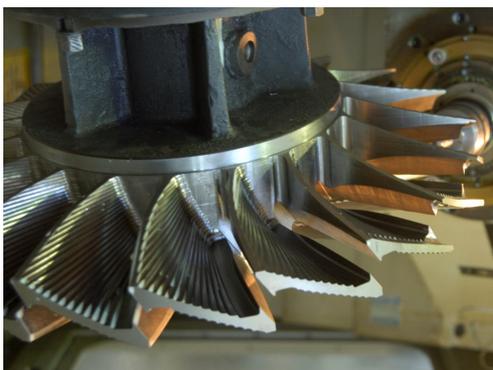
Предварительно обработанная заготовка моноколеса перед чистовой обработкой на станке ТВ-1005 ЛЕСНТИ
